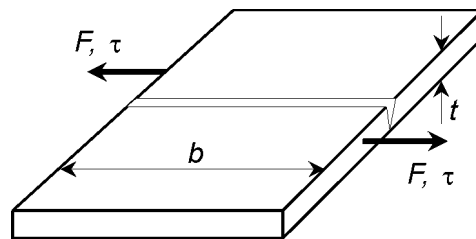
Soldadura a tope, tensiones de cortadura
